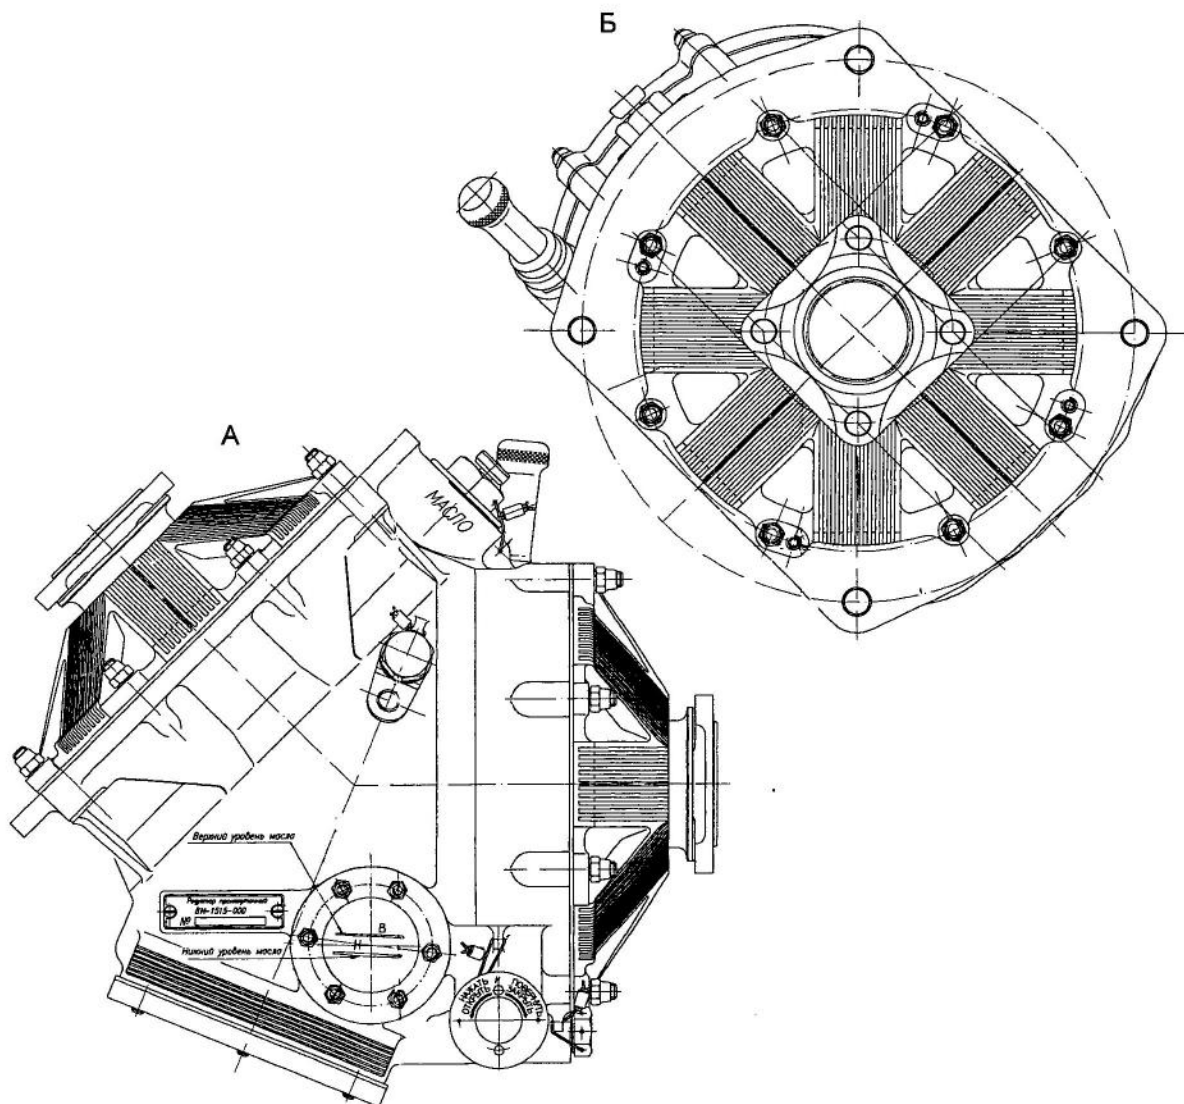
(Лист 2 из 3) Редуктор промежуточный
